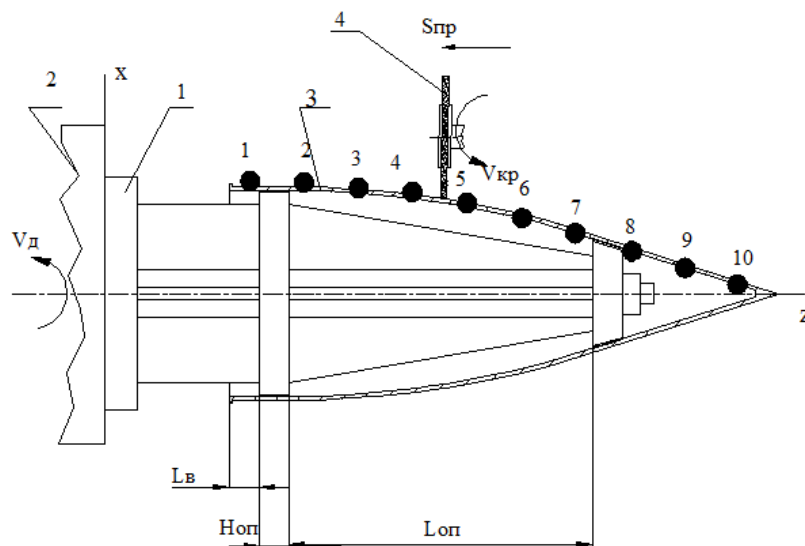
Схема установки заготовки на операции наружного шлифования изделия:
